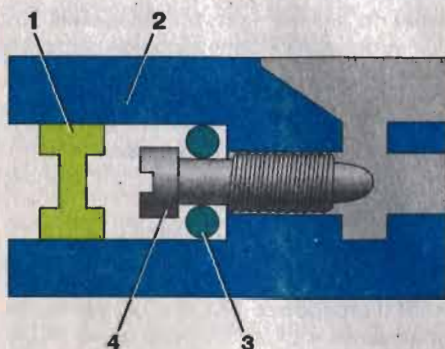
Схема установки заглушки канала расположения винта регулировки качества горючей смеси: 1 - заглушка; 2 - корпус карбюратора; 3 - уплотнительное кольцо; 4 - винт регулировки качества горючей смеси
